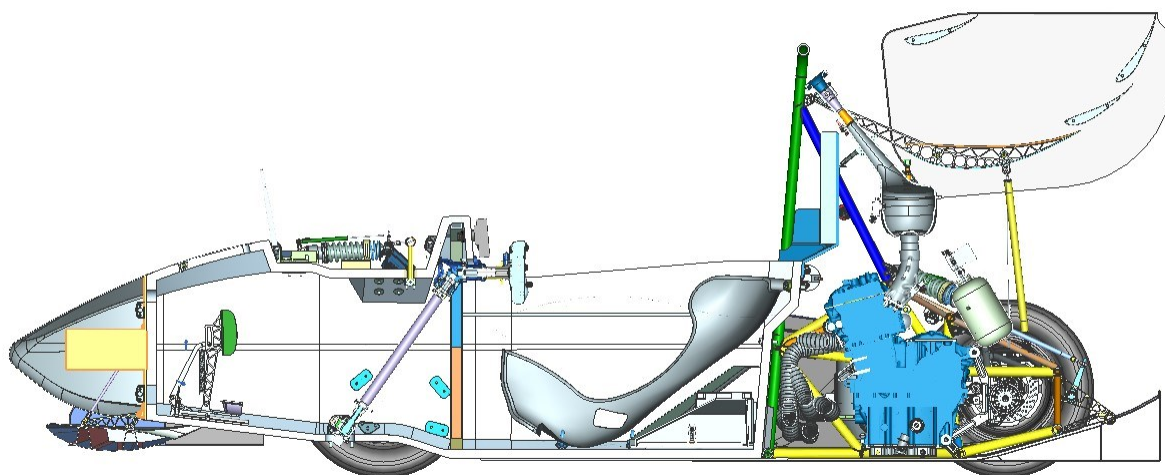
Příklad hybridního rámu vozu UWB06
